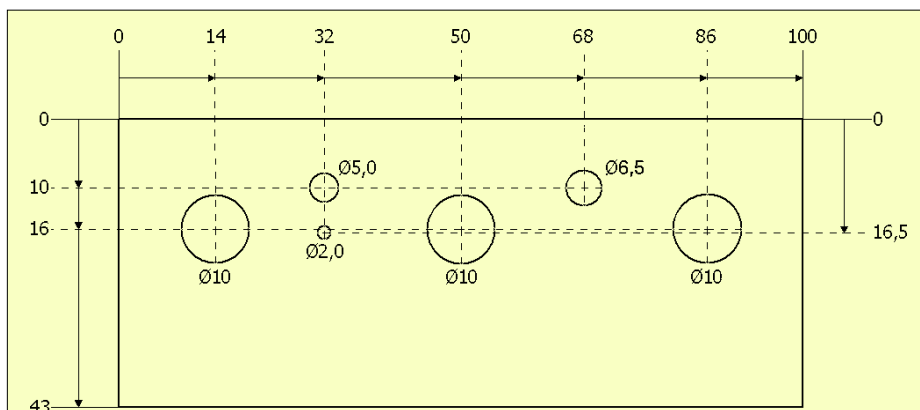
Maßskizze der Frontplatte für das realisierte Gehäuse
